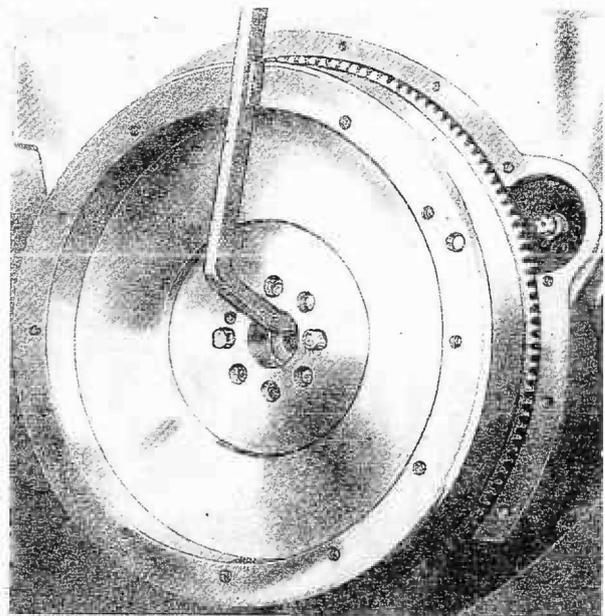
Schwungrad mit Hebezeug auf Hilfschrauben aufsetzen
